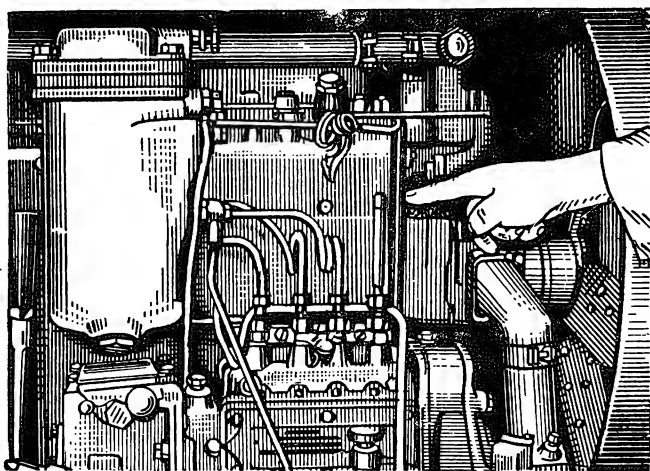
Трубка для проверки начала подачи топлива по мениску
